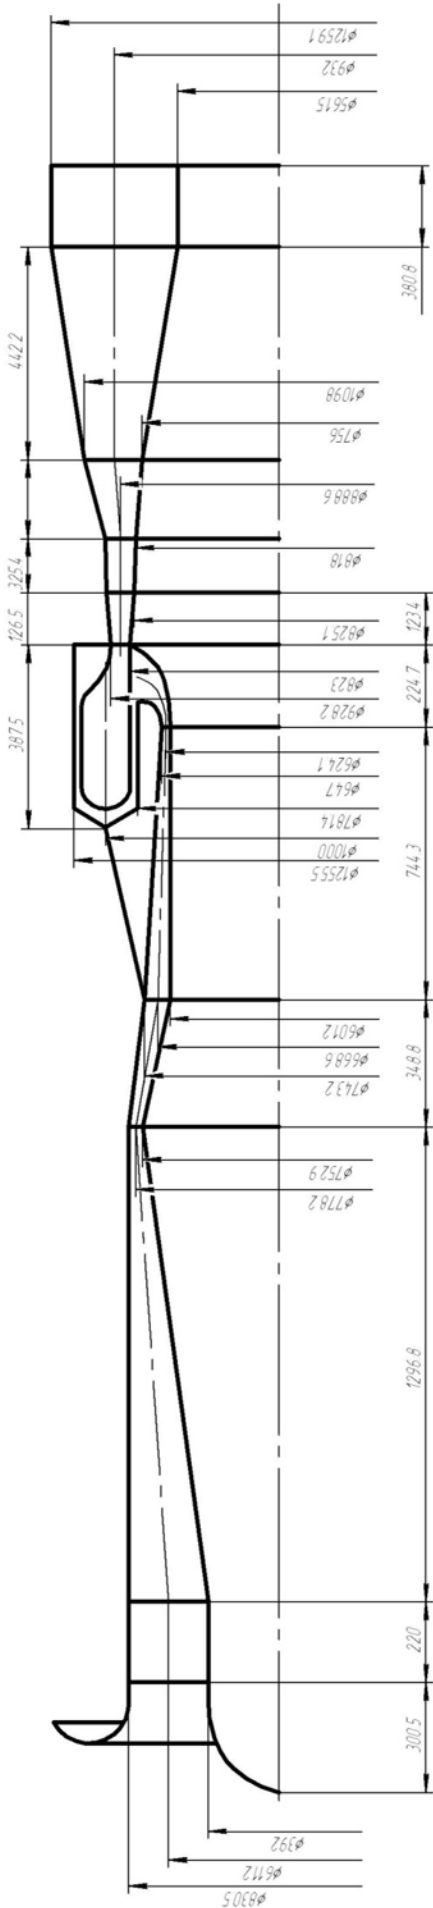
Ескіз меридіанального перетину ГТД
